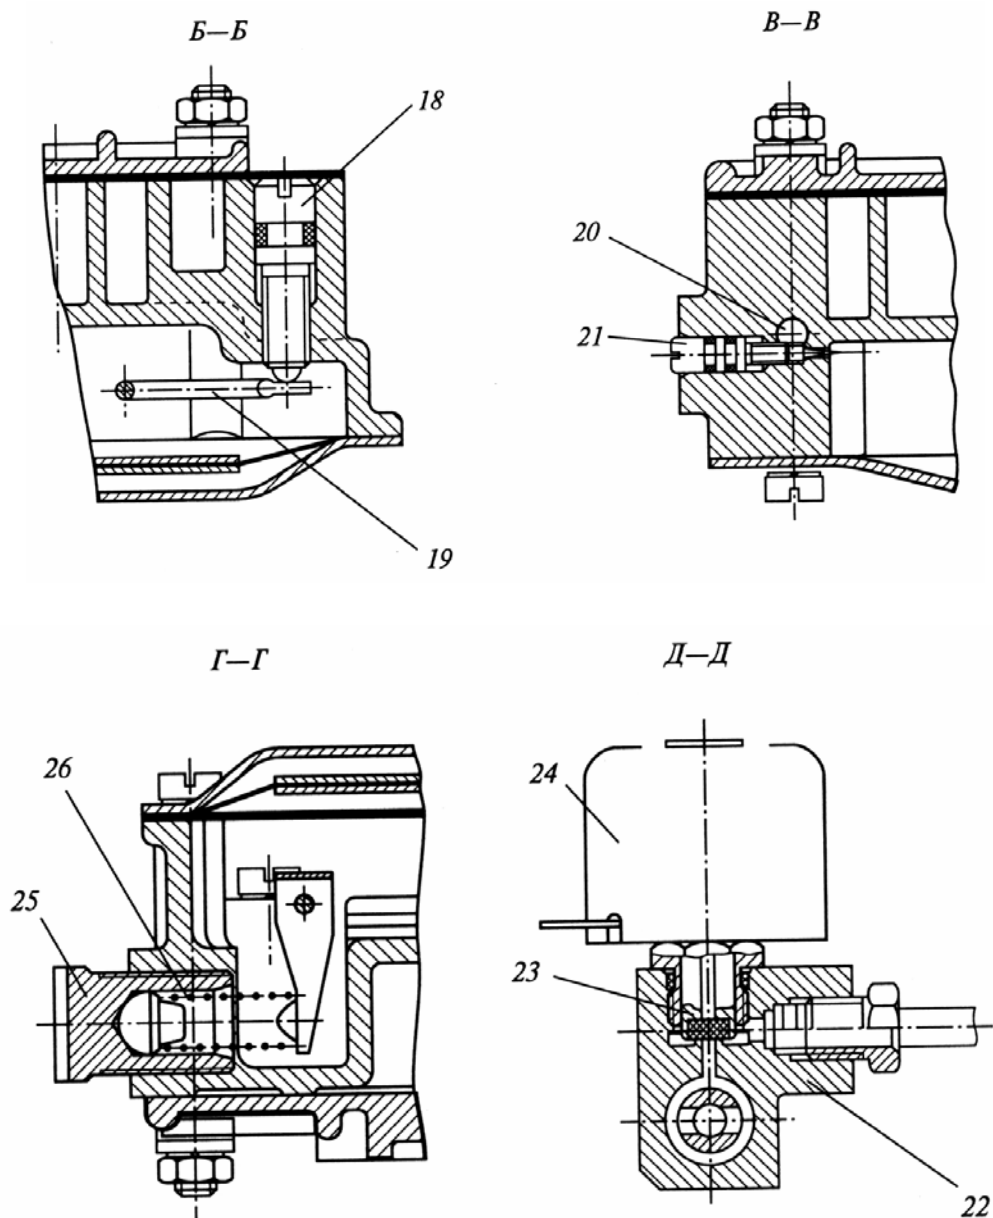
Конструкция редуктора-испарителя низкого давления
